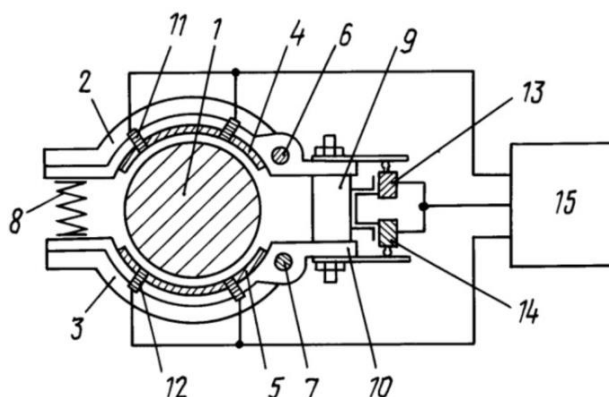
Устройство для осуществления контроля работы колодочного тормоза
